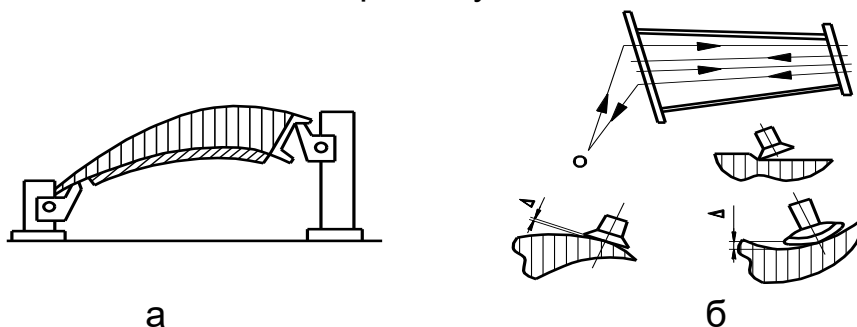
Схеми базування (а) і оброблення (б) стільникового блока
